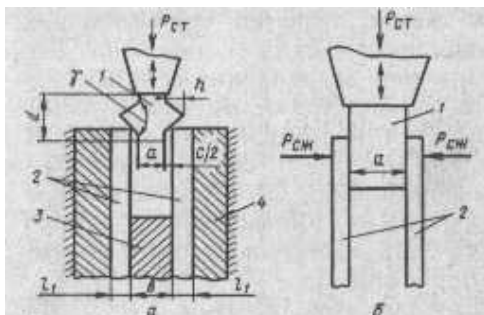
Ультразвуковая сварка впрессовкой в постоянный (а) и переменный (б) зазор: 1 - соединительный элемент-вкладыш; 2 - соединяемые пластины; 3 - установочный вкладыш; 4 - кондуктор;  $\gamma$  - угол V-образного выступа; d - высота соединительного элемента-вкладыша; h - высота V-образного выступа; l - толщина соединительных пластин
